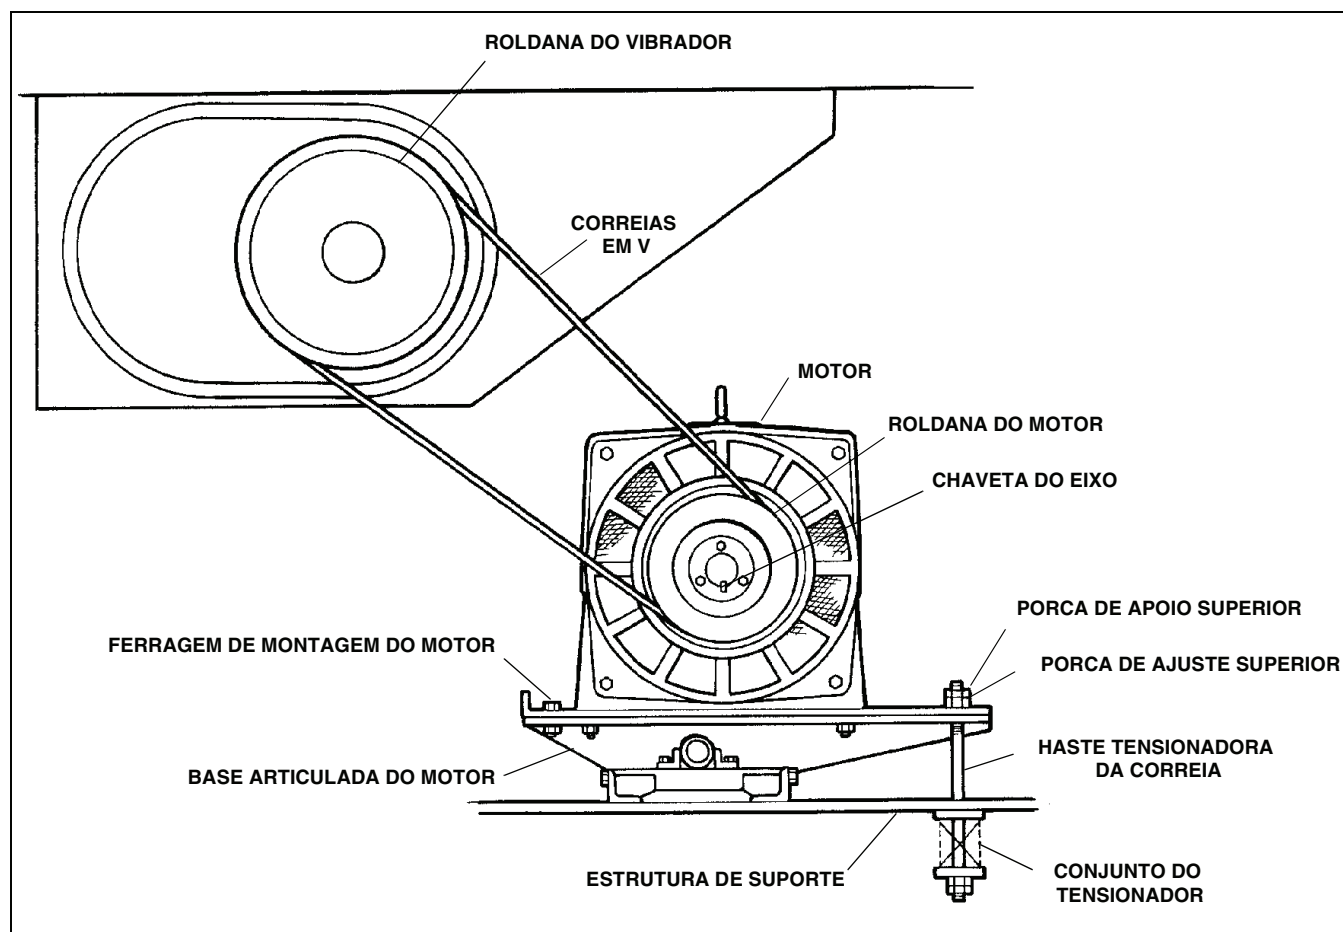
Conjunto do Motor de Transmissão Elétrica
